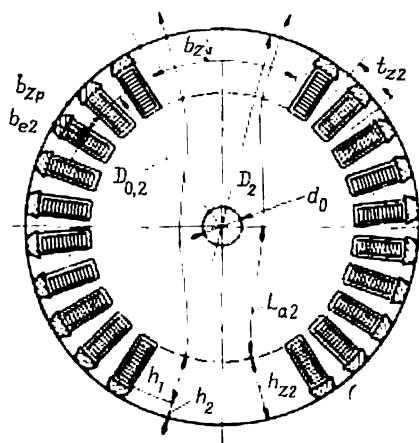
Dimensions de la zone active du rotor d'une machine à pôles lisses.
